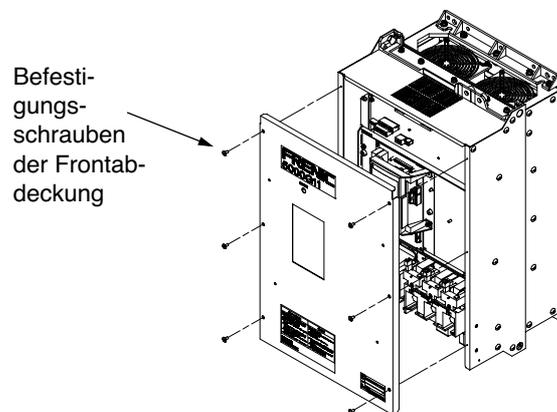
Abnehmen der Frontabdeckung (bei Frequenzumrichtern mit einer Leistung ab 30 kW)
